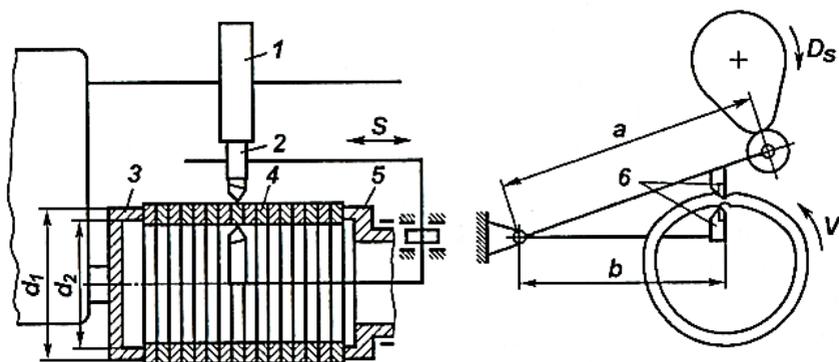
Схема копировального устройства для обработки заготовок колец:
